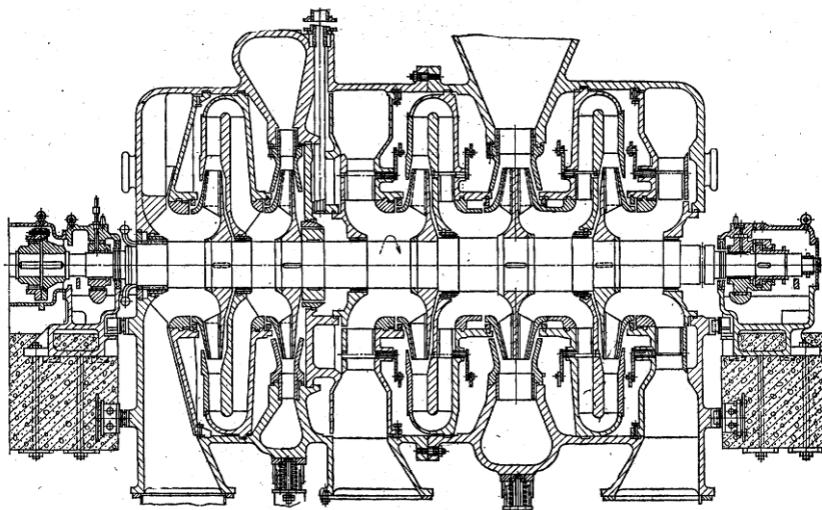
Центробежный шестиступенчатый компрессор типа «К»
